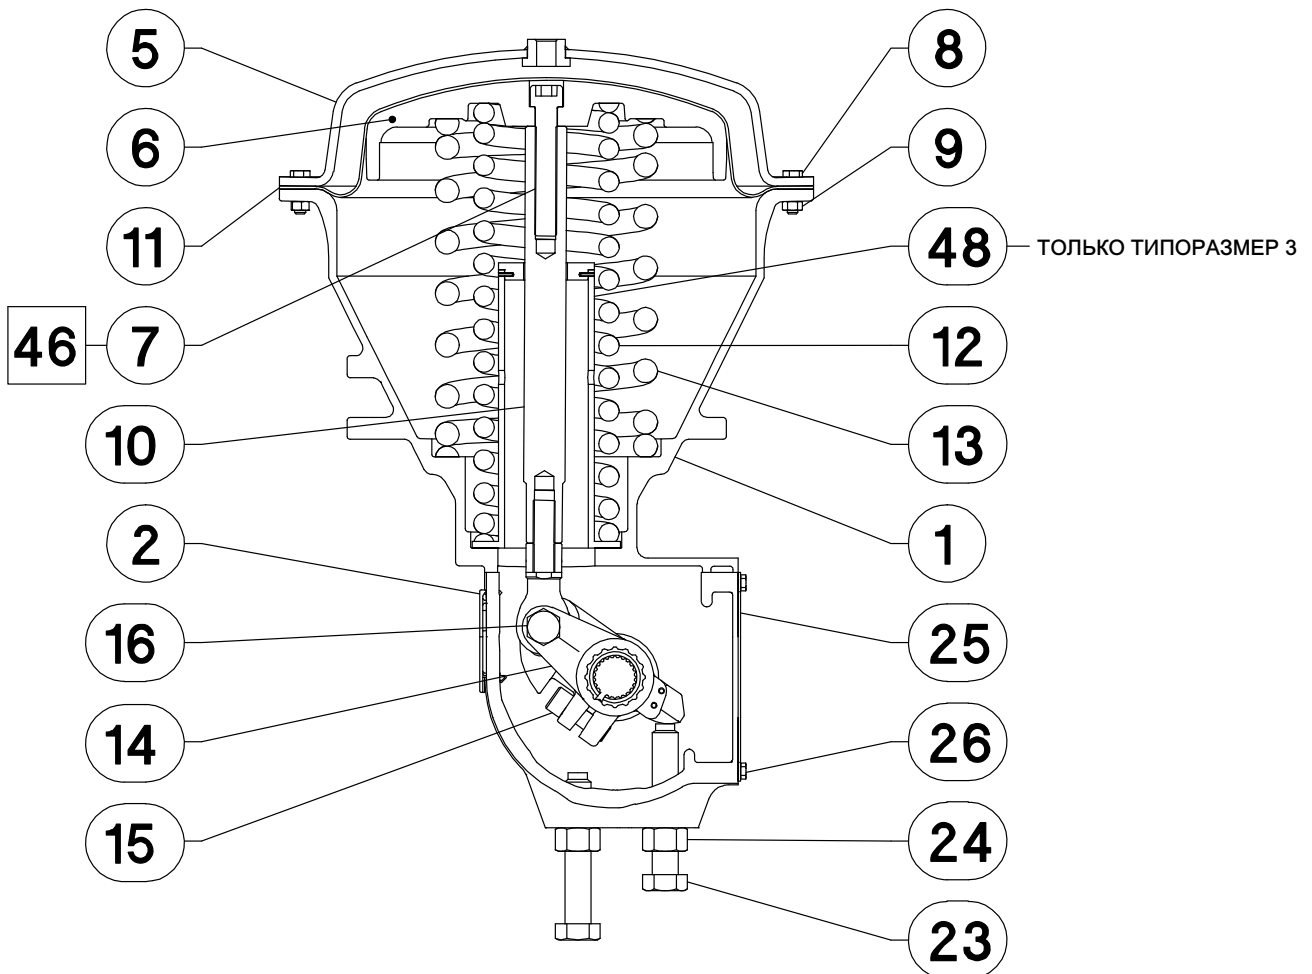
Привод Fisher 2052 типоразмера 3 в сборе
